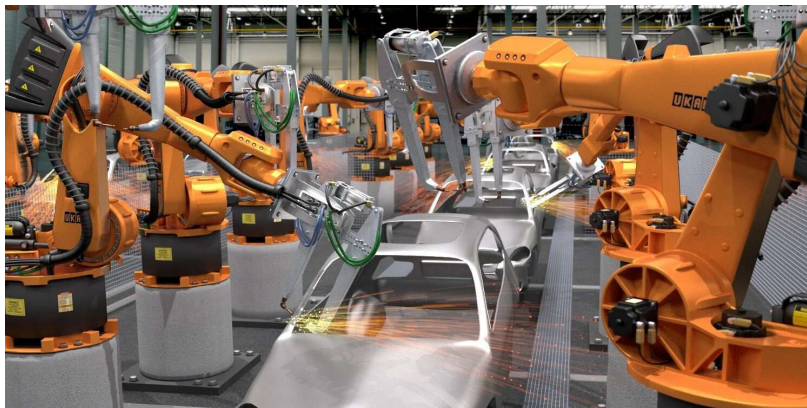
Robots de base fija realizando tareas de soldadura
